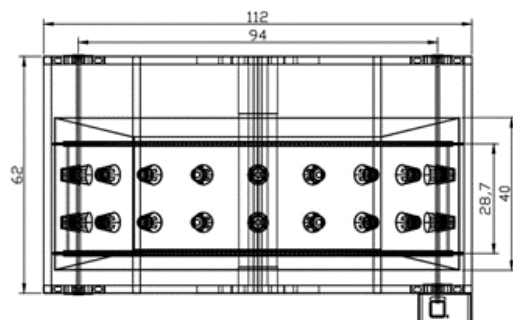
(a) Ukuran dan Skala Desain *Prototype* Tampak Atas
